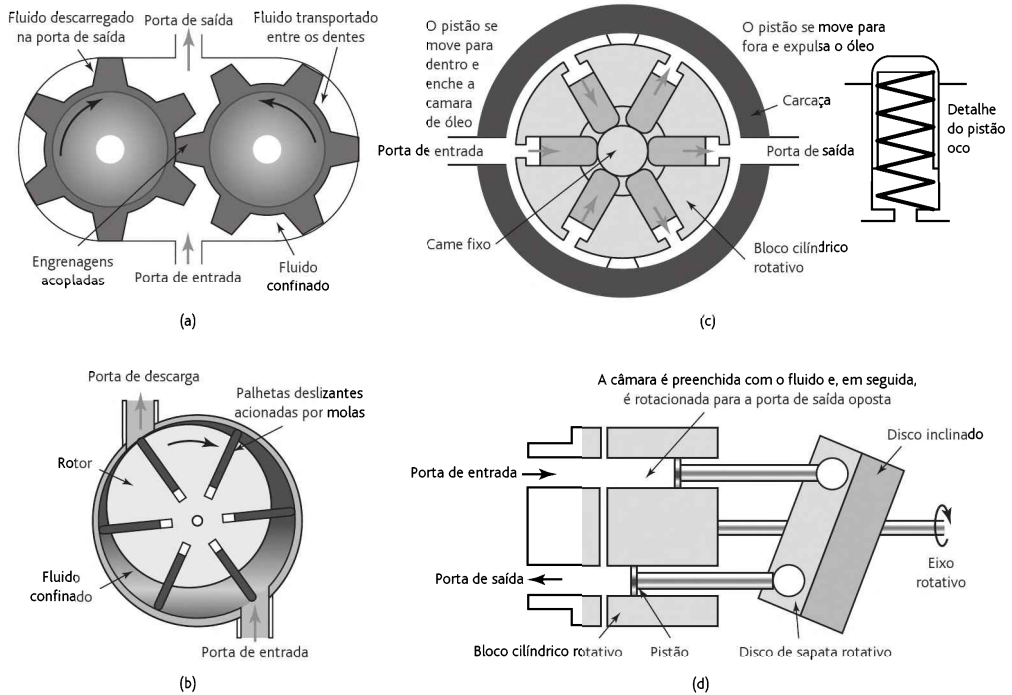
(a) Bomba de engrenagens, (b) bomba de palhetas, (c) bomba de pistão radial, (d) bomba de pistão axial com disco inclinado.
